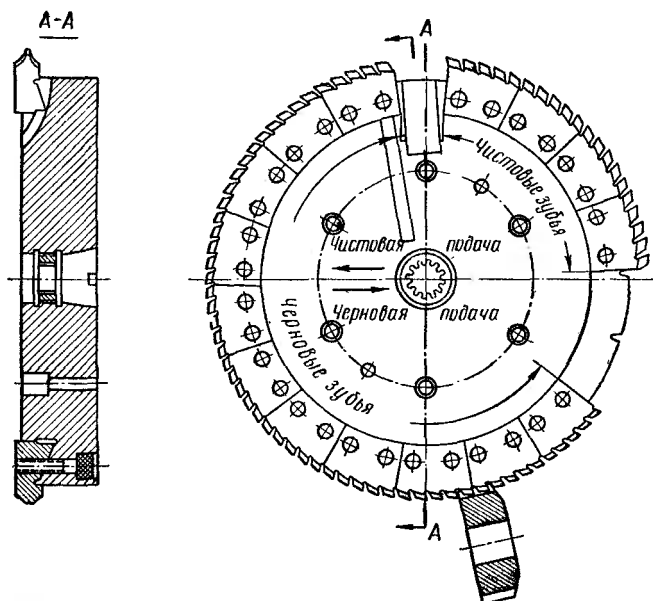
Круговая протяжка для нарезания зубьев конических зубчатых колес
